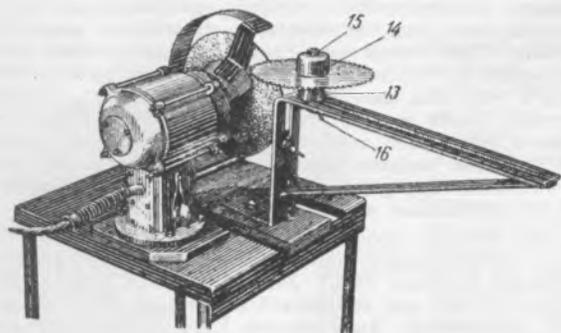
Приспособление к электроточилу для заточки круглых пил: 13 — металлический конус; 14 — стаканообразная шайба; 15 — закрепительный болт шайбы конуса; 16 — закрепительная гайка с барашком металлического конуса.
